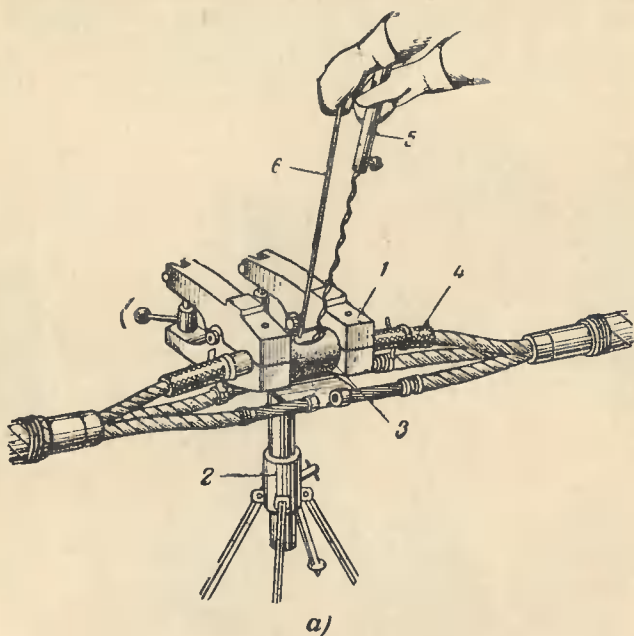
Термитная сварка алюминиевых жил кабеля.
